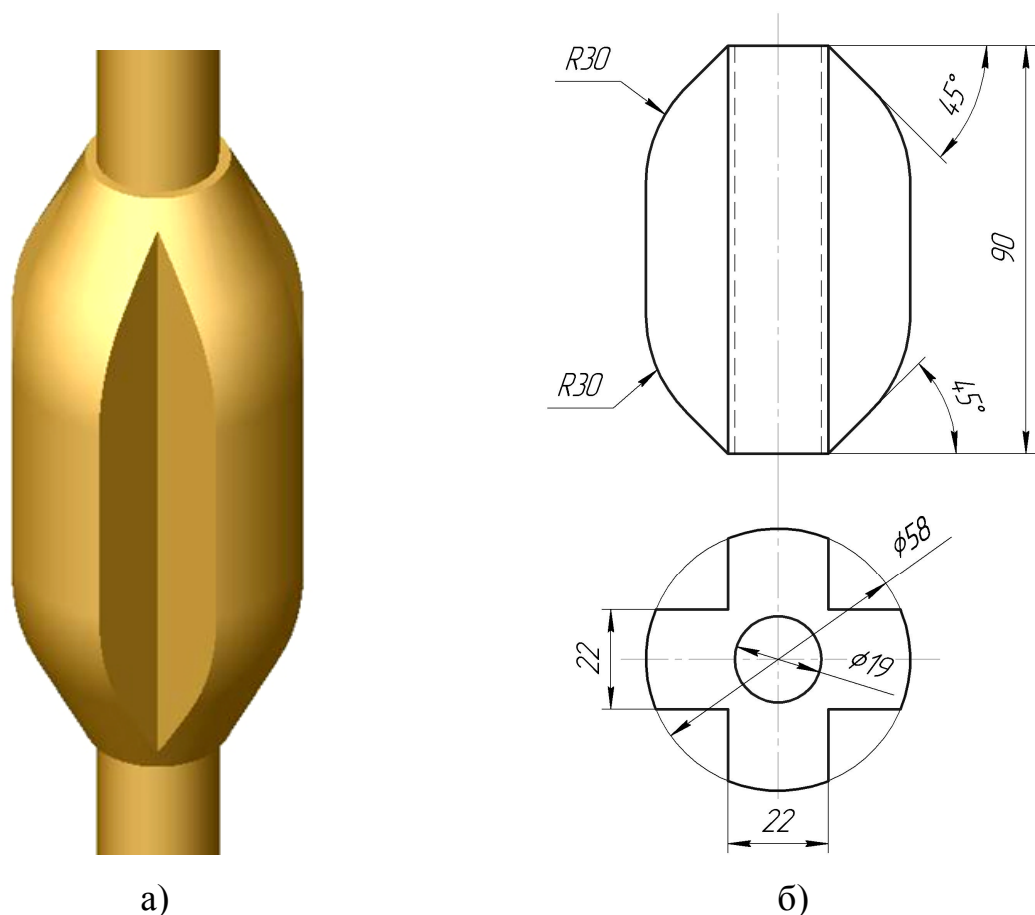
Протектор моделі Stealth™ фірми The Endurance™ (США): загальний вигляд (а), і схема з розмірами (б)
